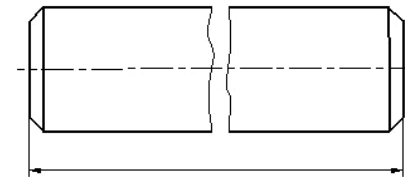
Пример обозначение размера при изображении детали с разрывом
